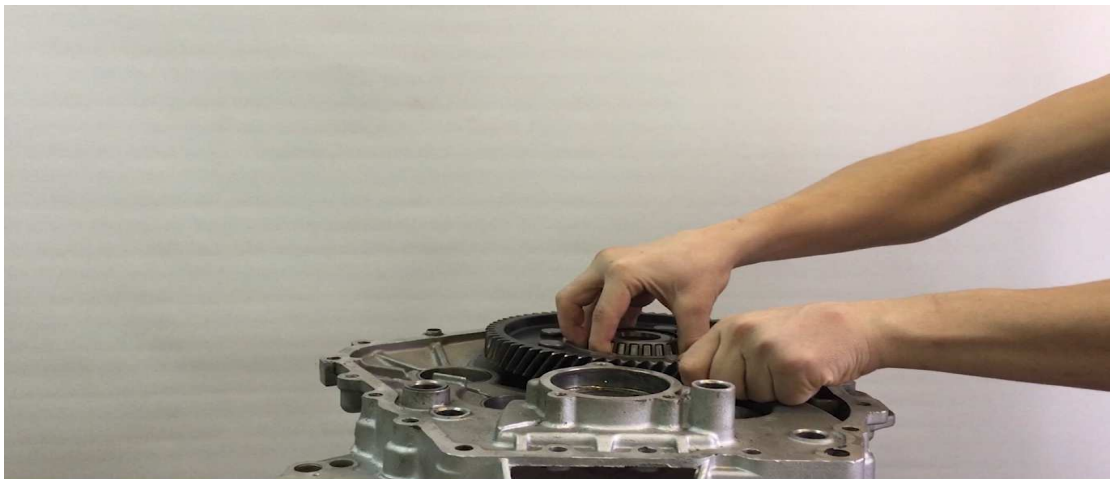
Установка основных комплектующих деталей в картер коробки передач.
